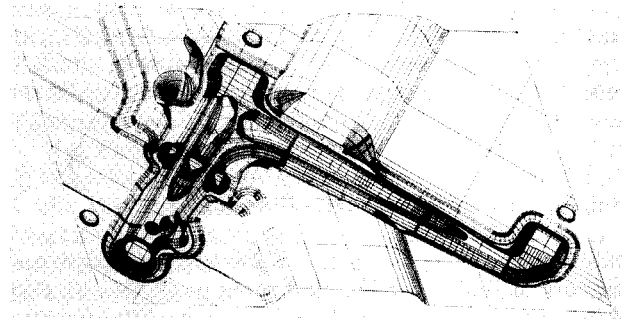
Querlenker; CAD-Geometrie für Vorpreßgesenk
